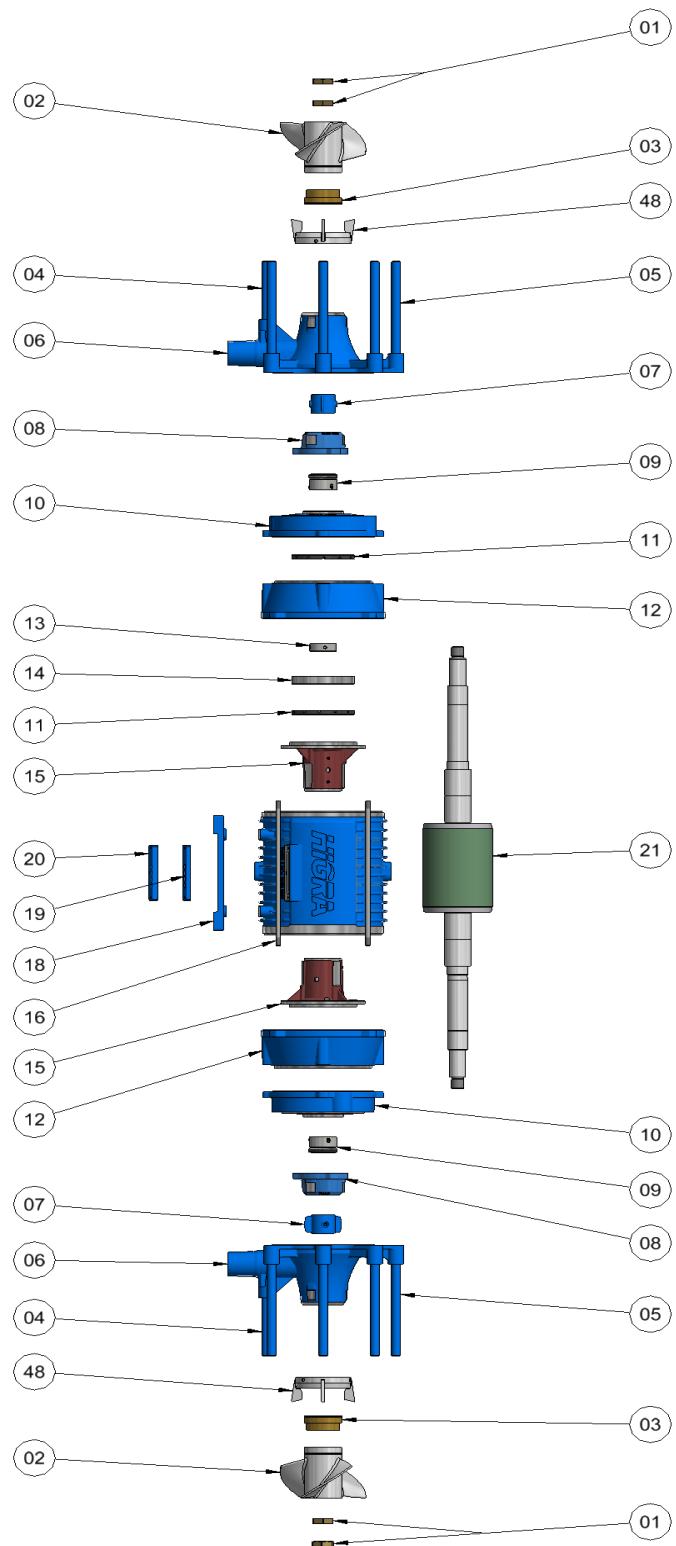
Vista explodida do Conj. Motor Tornado Biturbo.
